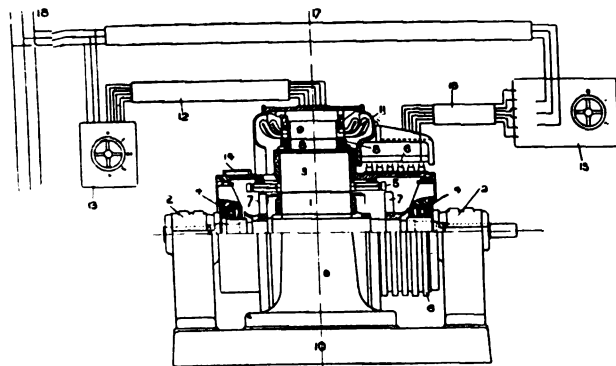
Coupe axiale de moteur à rotor intermédiaire.
